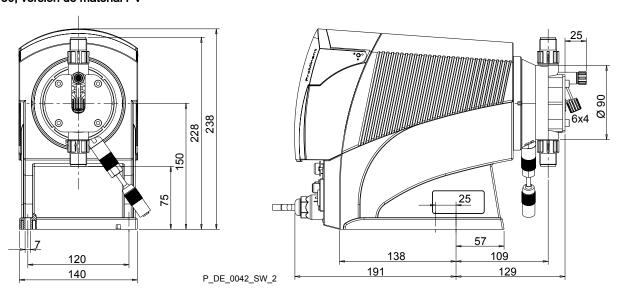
Hoja de dimensiones del tipo delta® 1612 - 0730, versión de materiales PV; dimensiones en mm
